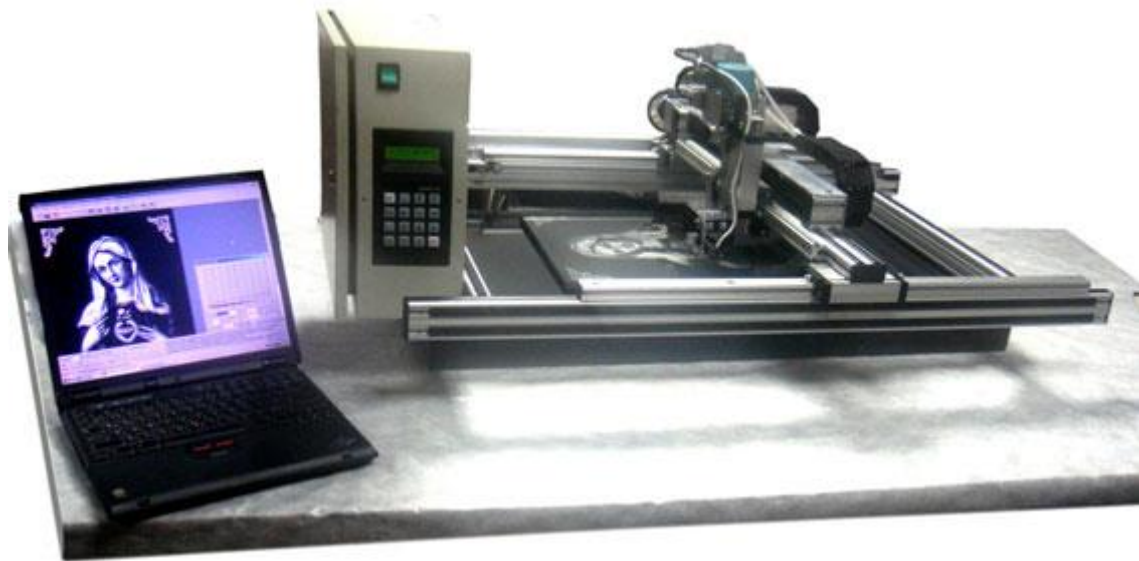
Гравировальный станок-автомат «График-ЗКП» (вариант установки станка на большие по площади заготовки, ножки сняты, станок лежит на поверхности заготовки).
